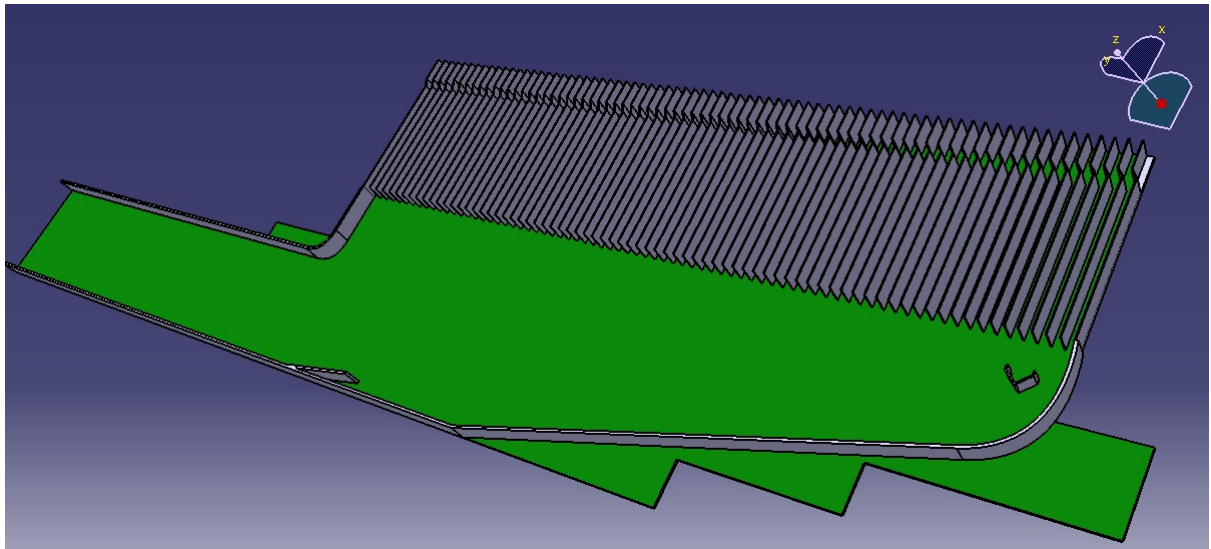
Pressure breaker sur la table d'entrée de la laveuse bouteilles du groupe 1 -
